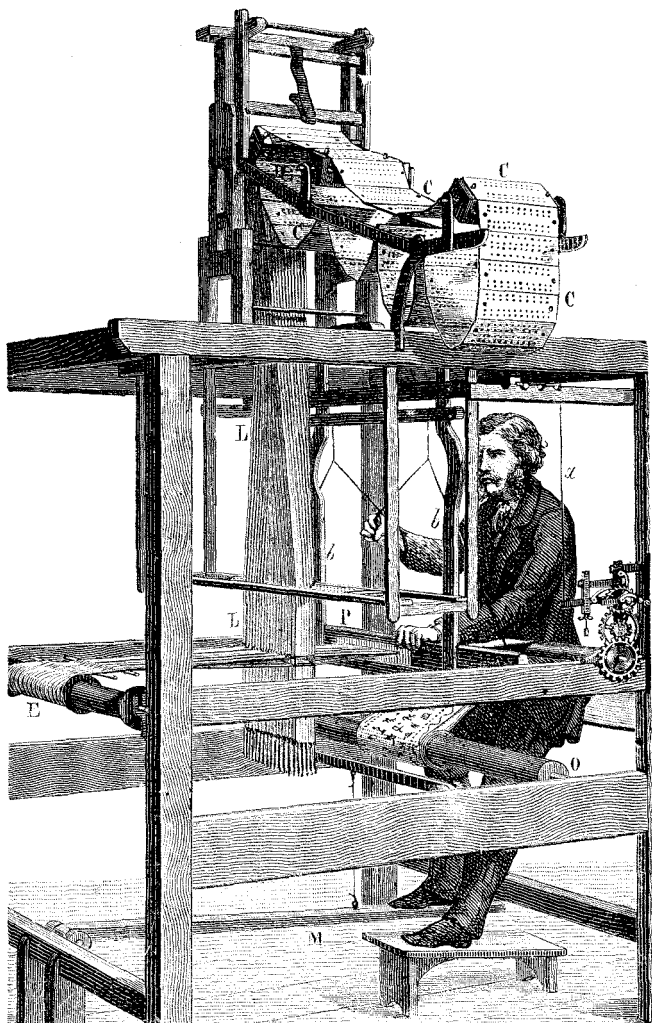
Conjunto da machina de tecer, de Jacquard.
